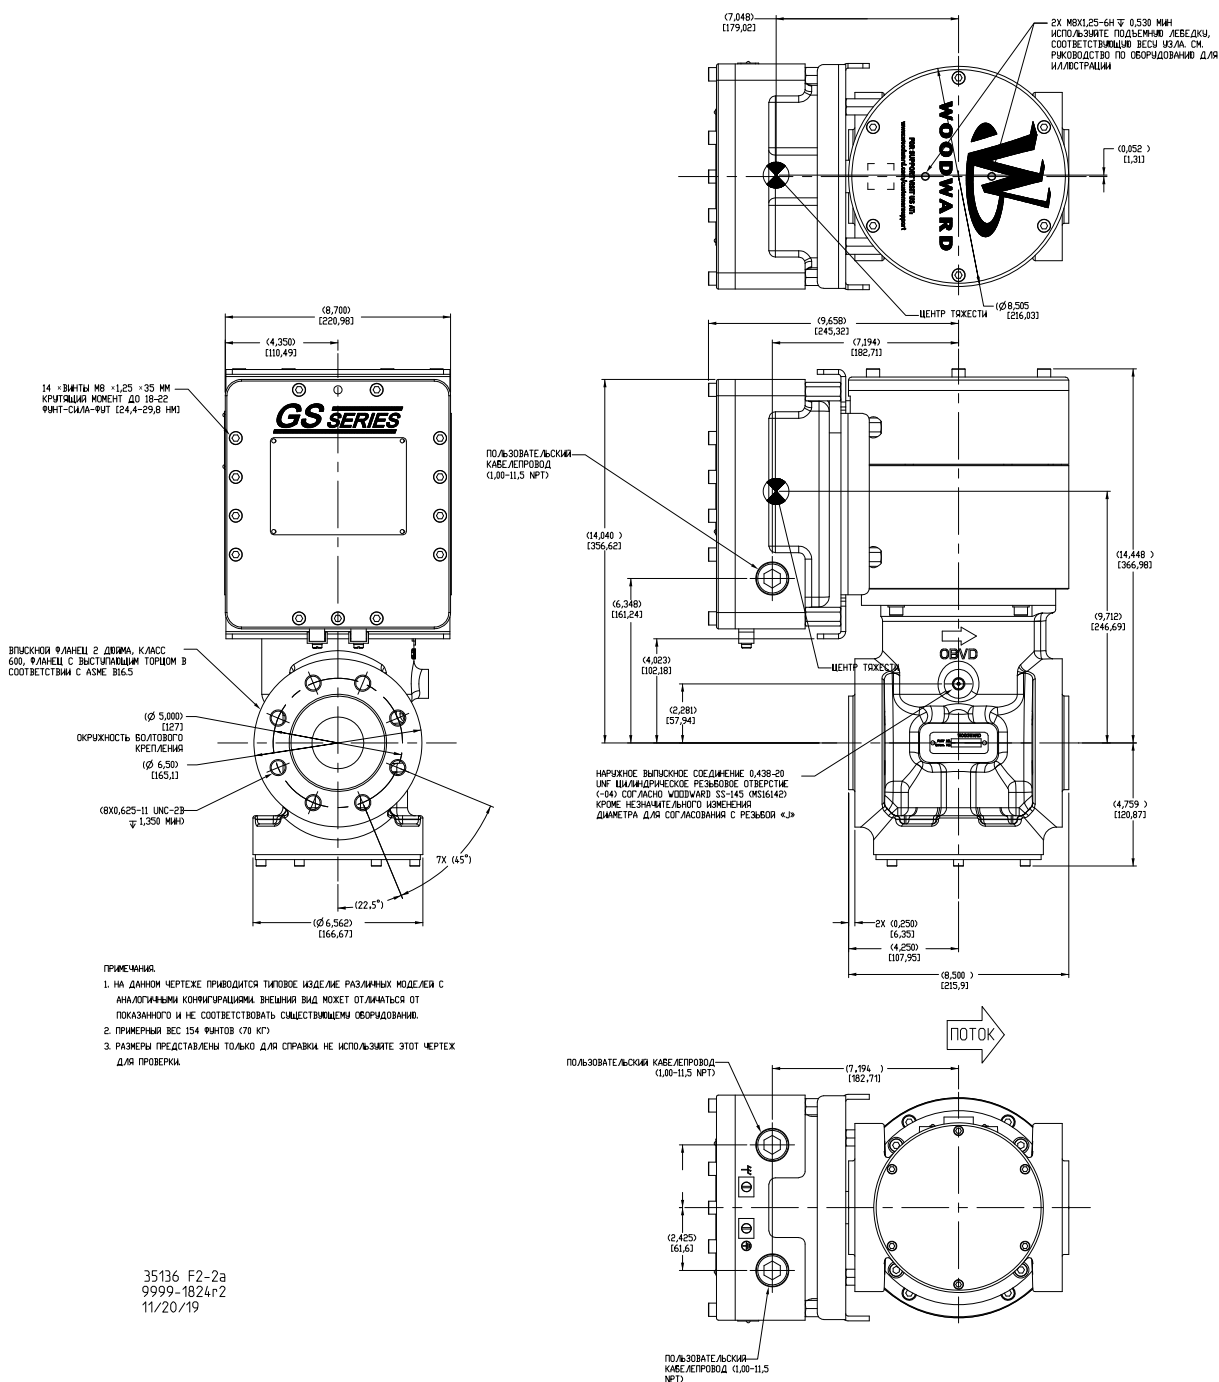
а. Габаритно-присоединительный чертеж, нержавеющая сталь, GS50, с кабельными вводами
